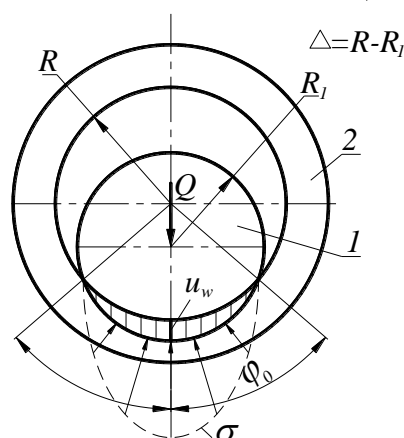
Розрахункова схема циліндричного підшипника ковзання
